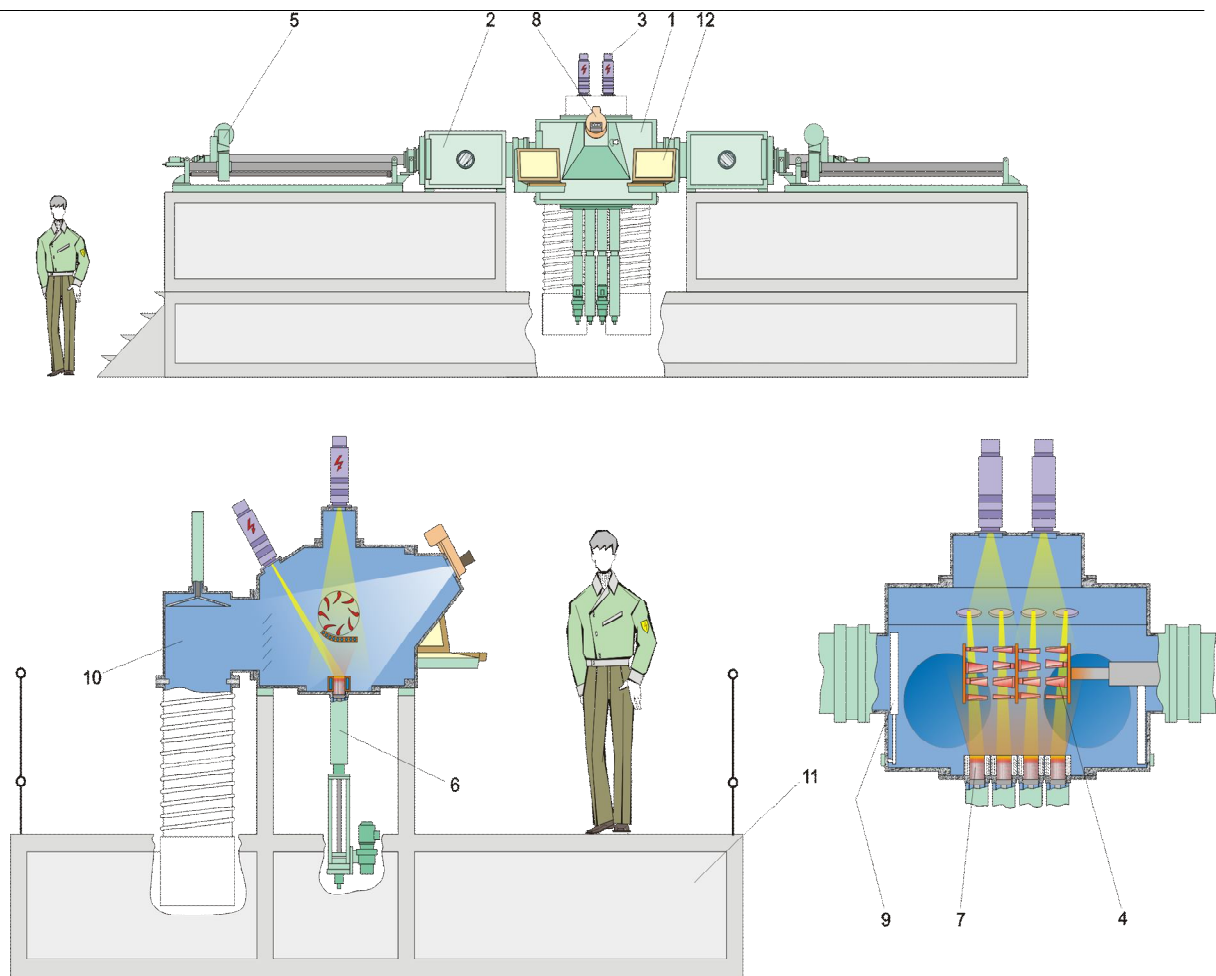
Общий вид установки Л-9 и схема нанесения покрытий: 1 – технологическая камера; 2 – шлюзовая камера; 3 – ЭЛ пушка; 4 – кассета; 5 – механизм подачи кассеты; 6 – механизм подачи слитка; 7 – тигель; 8 – смотровая система; 9 – заслонка; 10 – вакуумная система; 11 – площадка обслуживания; 12 – пульт управления
